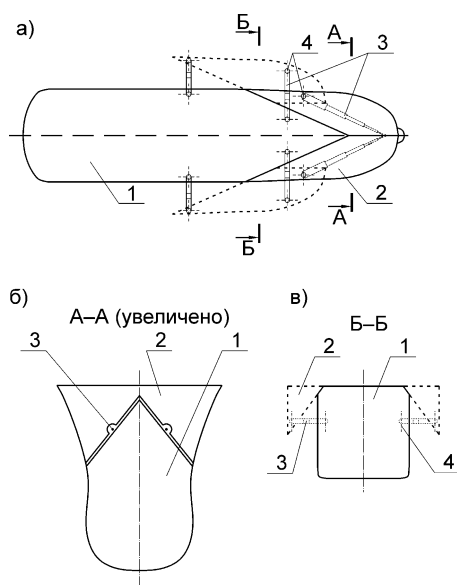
Конструкция корпуса судна с изменяемой геометрией носовой оконечности: а) – общий вид корпуса судна; б) – сечение А-А; в) – сечение Б-Б
